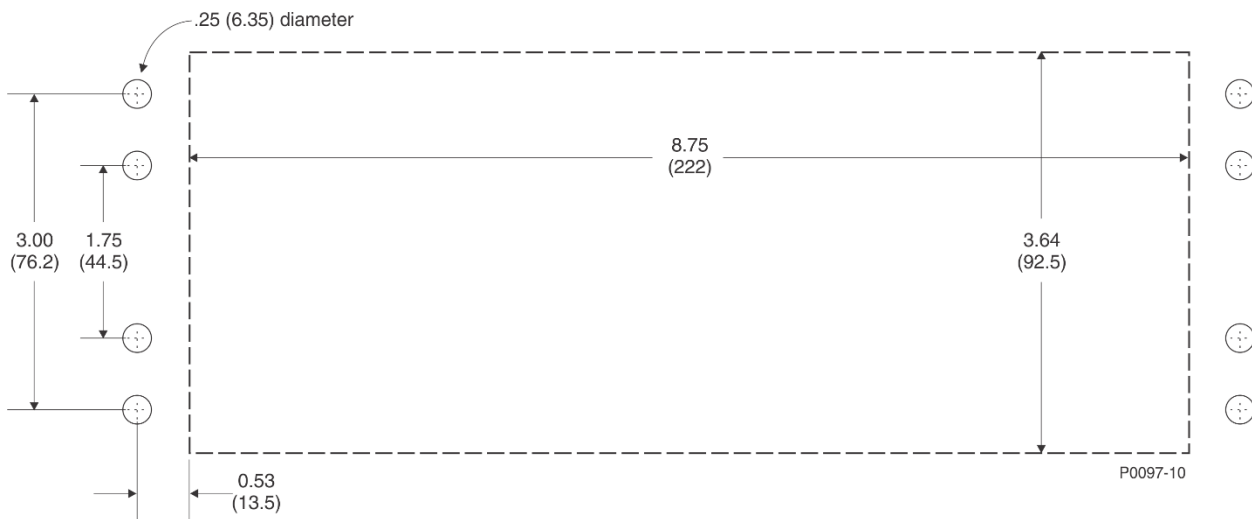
Dimensions de perçage et de découpe d'un BE1-11g H1 simple (boîtier de type H) pour montage en tiroir
